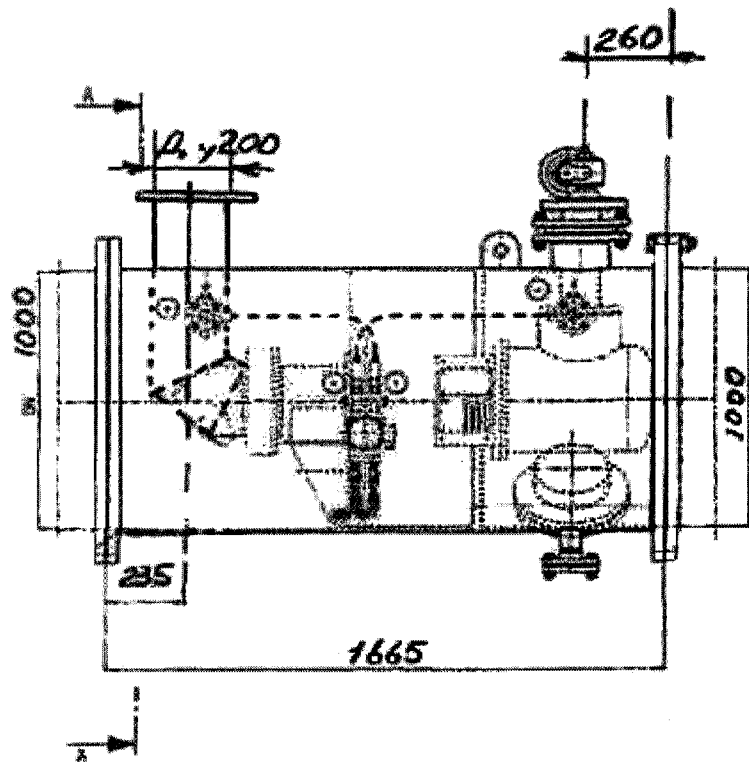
Габаритный чертеж фильтра-сетки РНН10АТ001, РНН10АТ002
